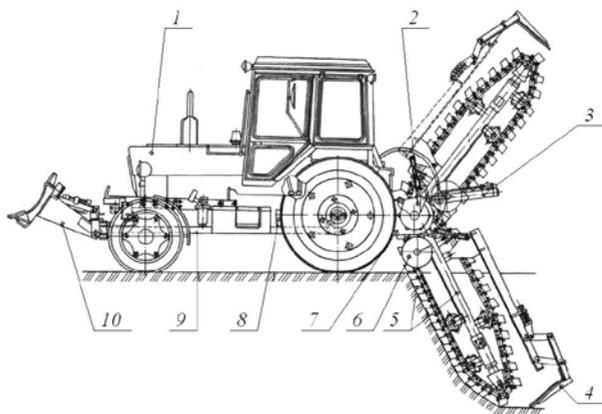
Экскаватор-траншеекопатель ЭТЦ-165А: 1 – трактор базовый; 2 – муфта предельного момента; 3 – гидроцилиндр механизма подъема; 4 – башмак зачистной; 5 – экскаваторное рабочее оборудование; 6 – шнеки; 7 – редуктор привода рабочего органа; 8 – ходоуменьшитель; 9 – рама; 10 – бульдозер универсальный
